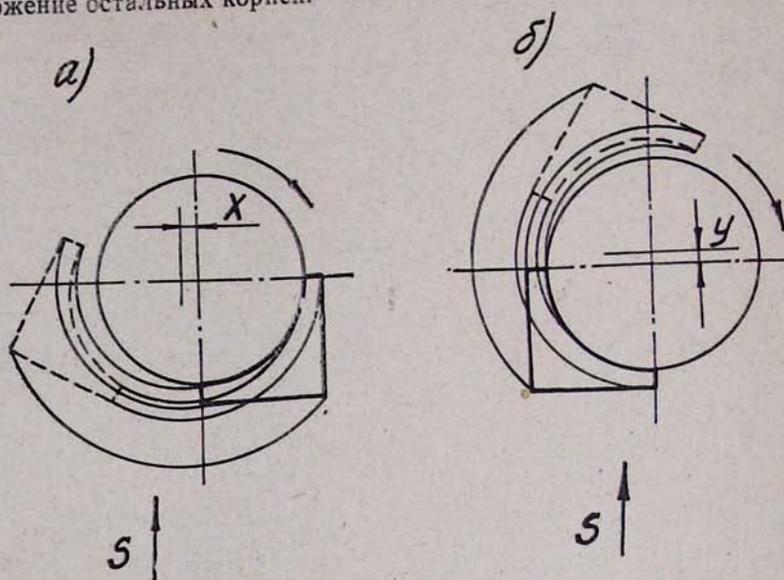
Схема взаимного расположения заготовки и фрезы.
